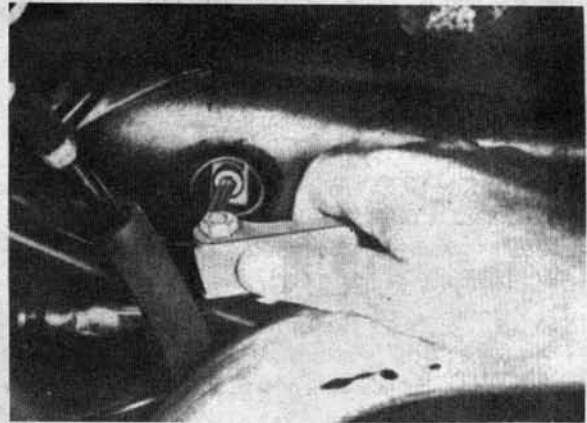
Отсоединение приводного вала от входного вала коробки передач в автомобилях с двигателями В19 и В200
